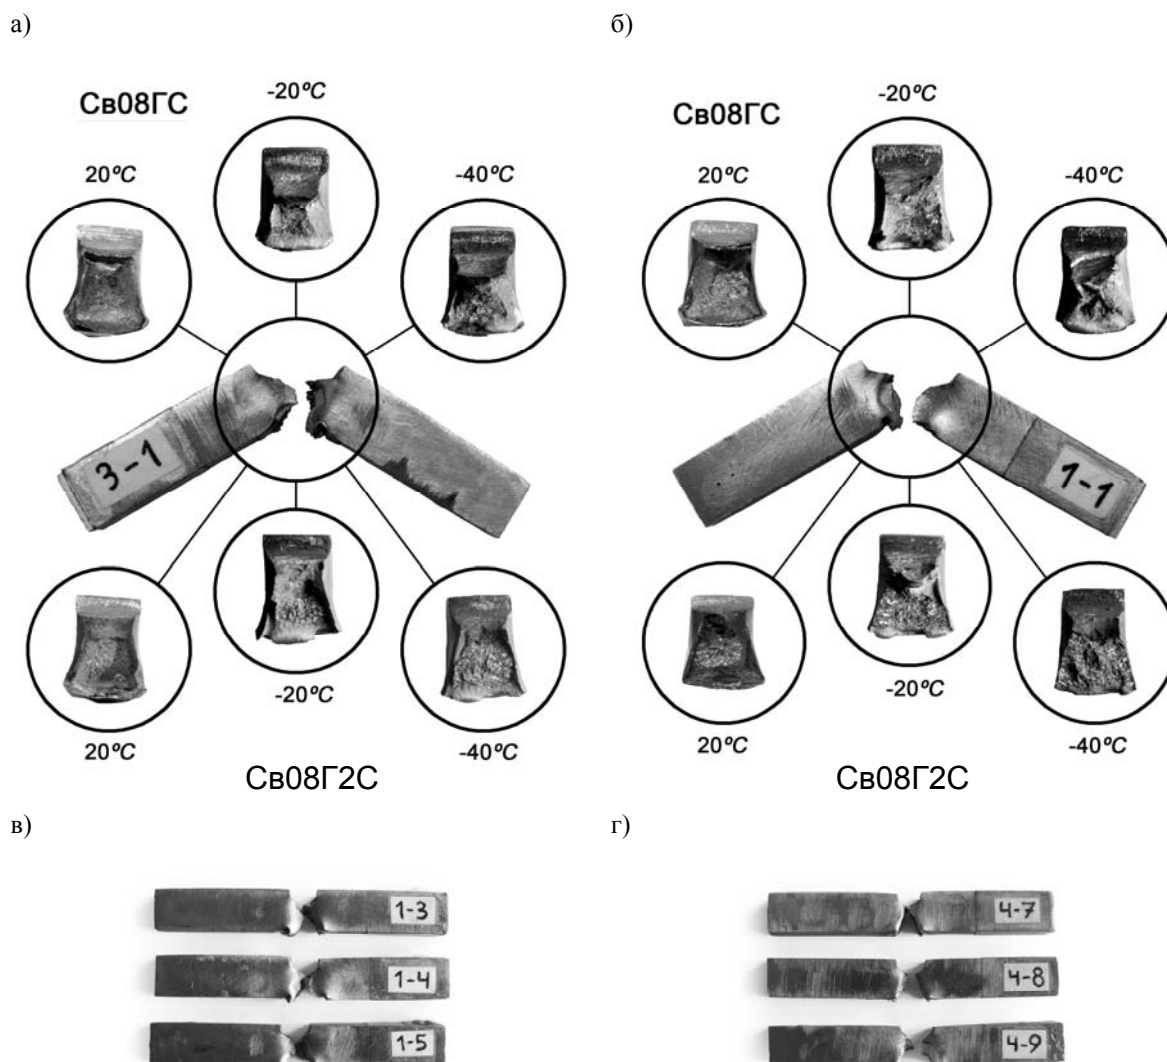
Внешний вид образцов после испытаний на ударный изгиб: а – сварка с двухструйной подачей газов в зону горения дуги; б – сварка в газовой смеси Ar + CO<sub>2</sub> по традиционной технологии; в – образцы с большой долей вязкого волокна в изломе; г – образцы с большой долей хрупкого волокна в изломе
